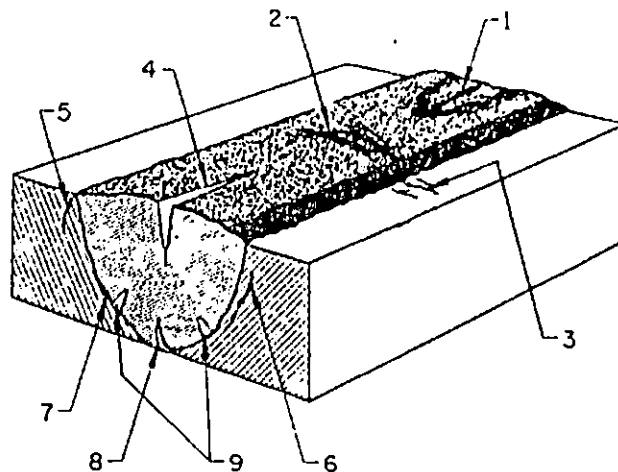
Esquemáticas de diversos tipos fracturas transversales, longitudinales, de cráter, de pie (es decir en la base de la soldadura) ¹¹⁻²¹
